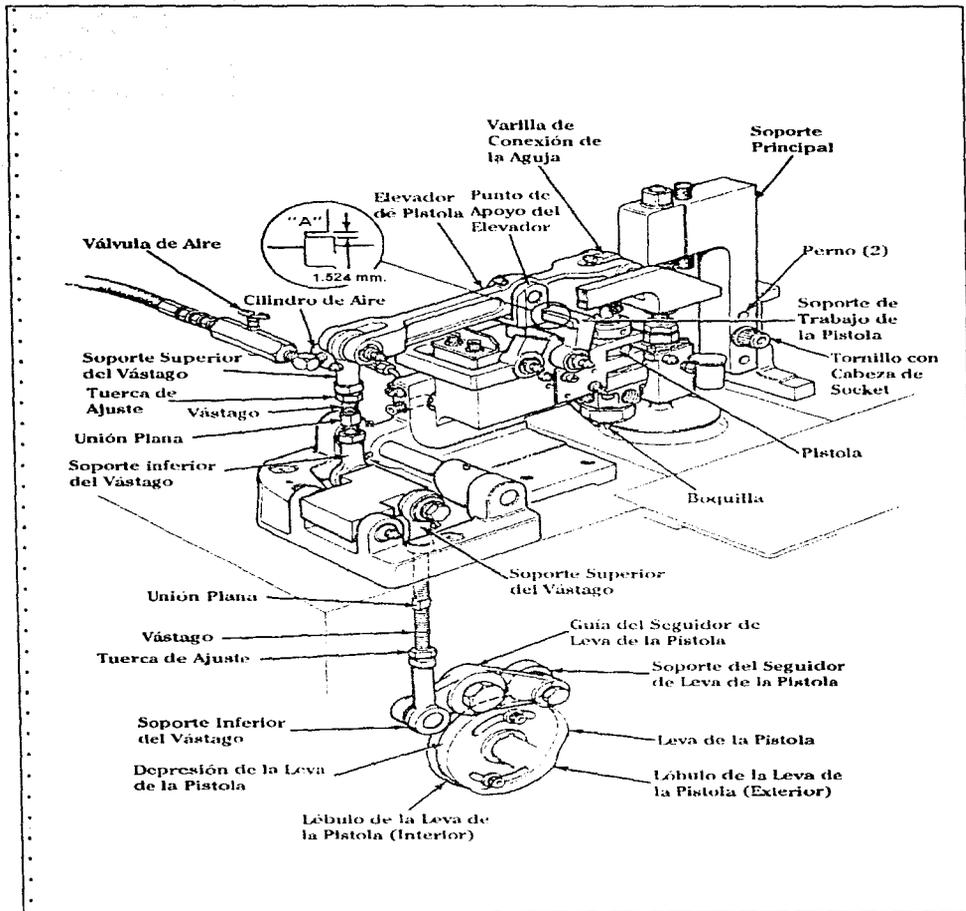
Esquema de una pistola mecánica para aplicación de compuesto sellador
